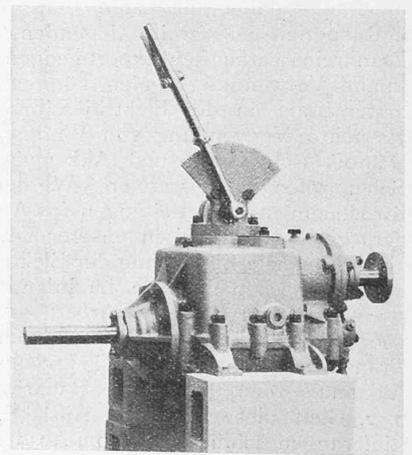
Flüssigkeits-Wechsel- und Wende-Getriebe, System Heinrich Schneider, für Werkzeugmaschinen- u. Hebezeug-Antriebe, gebaut von der Schweizer Lokomotivfabrik Winterthur.
